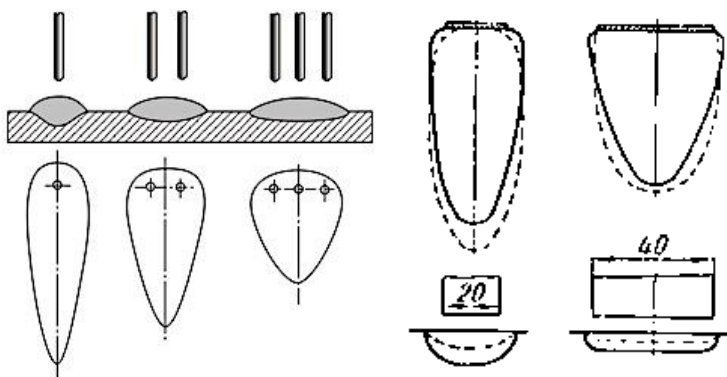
Форма ванны жидкого металла (в плане и максимальном поперечном сечении) при наплавке проволоками и лентой различной ширины на одинаковом режиме: ток 720 А, напряжение 32 В, скорость сварки 12 м/ч
